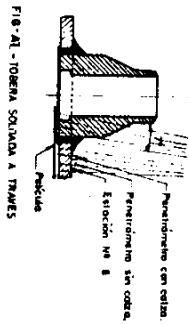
TORERA SOLDADA A TRAVÉS DE LA TORERA.
